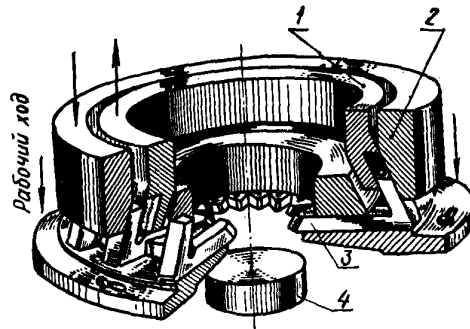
Зуборізна головка з різцями для контурного зубодовбання
